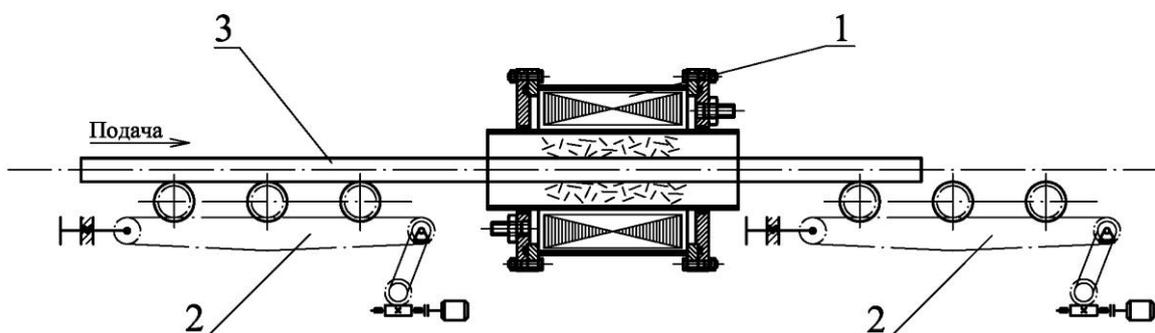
Схема обработки длинномерных деталей: 1 - рабочий блок устройства с ВЭМП; 2 - приводной ролик с роликами; 3 - деталь.
